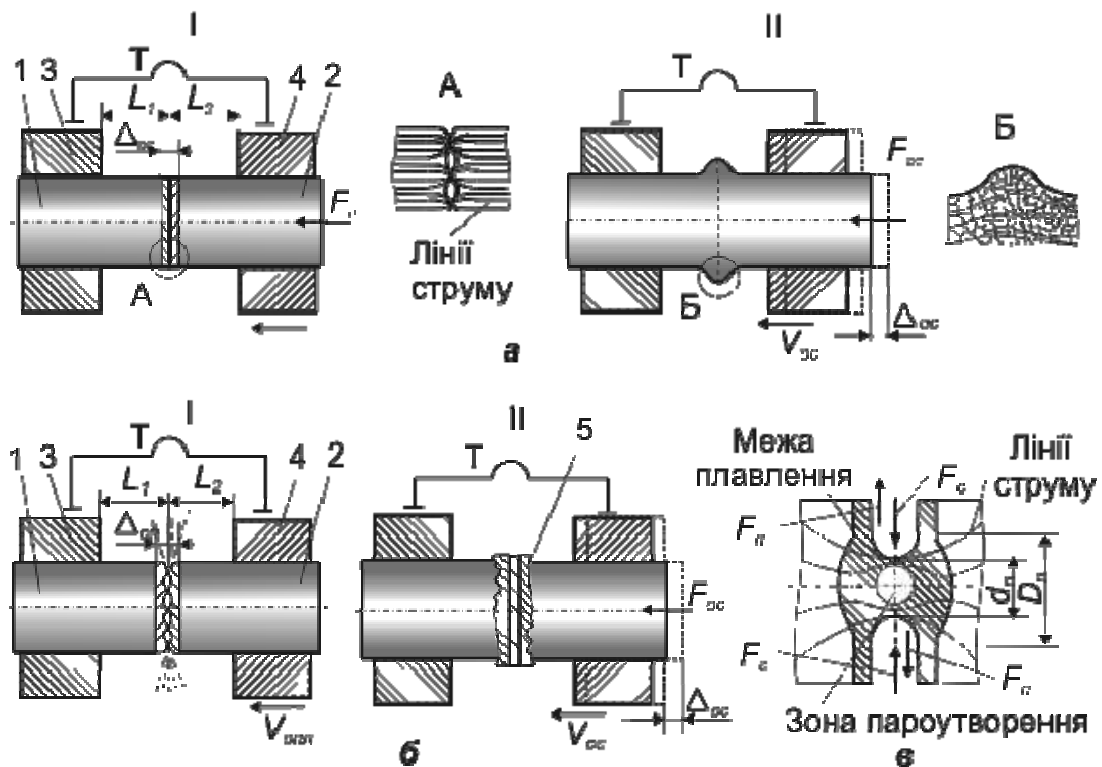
Схема стикового зварювання: а – опором; б – безперервним оплавленням; в – перемичка розплавленого металу при оплавленні; I – стик до зварювання; II – стик після зварювання
